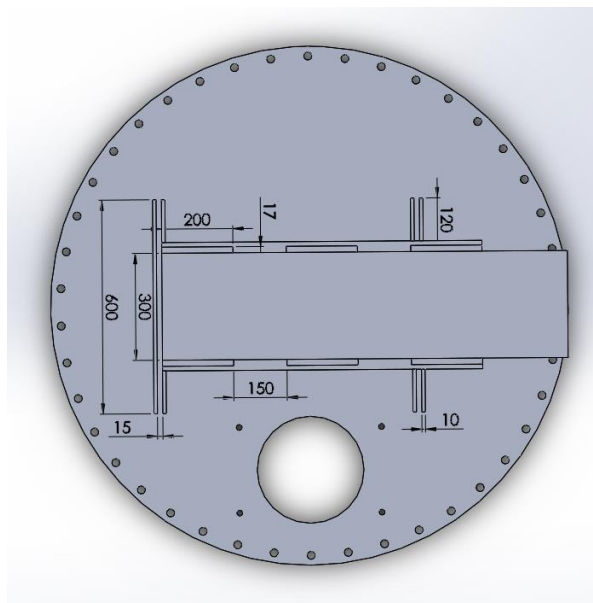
Distribución de los cordones de soldadura de la pluma.
